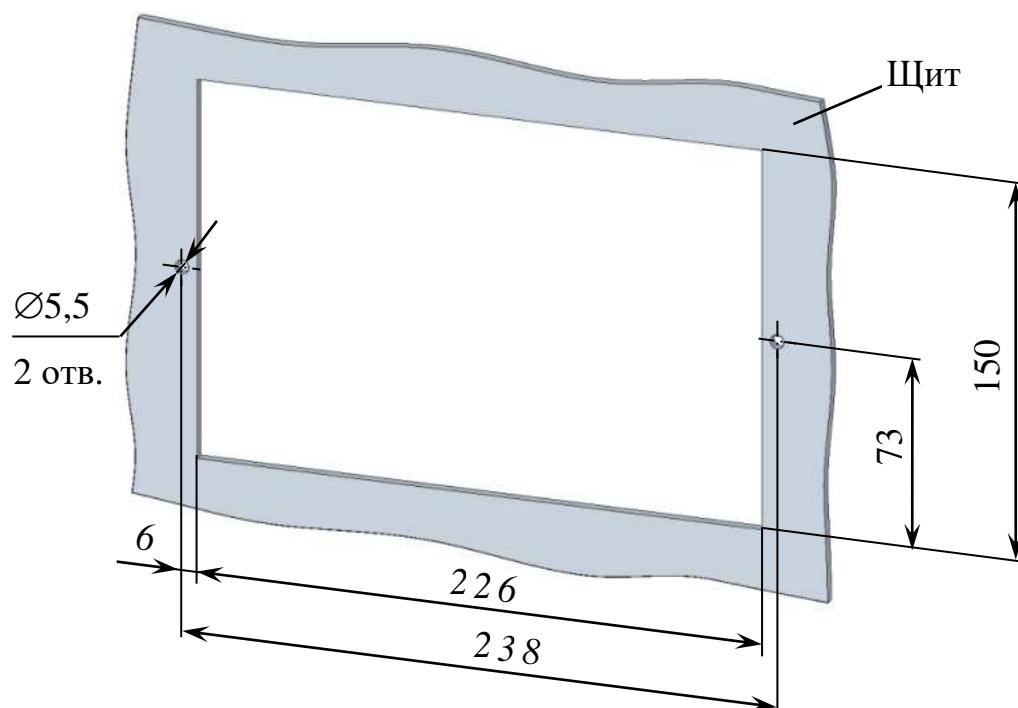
Расположение и размер отверстий для крепления блока преобразовательного щитового исполнения в щите
